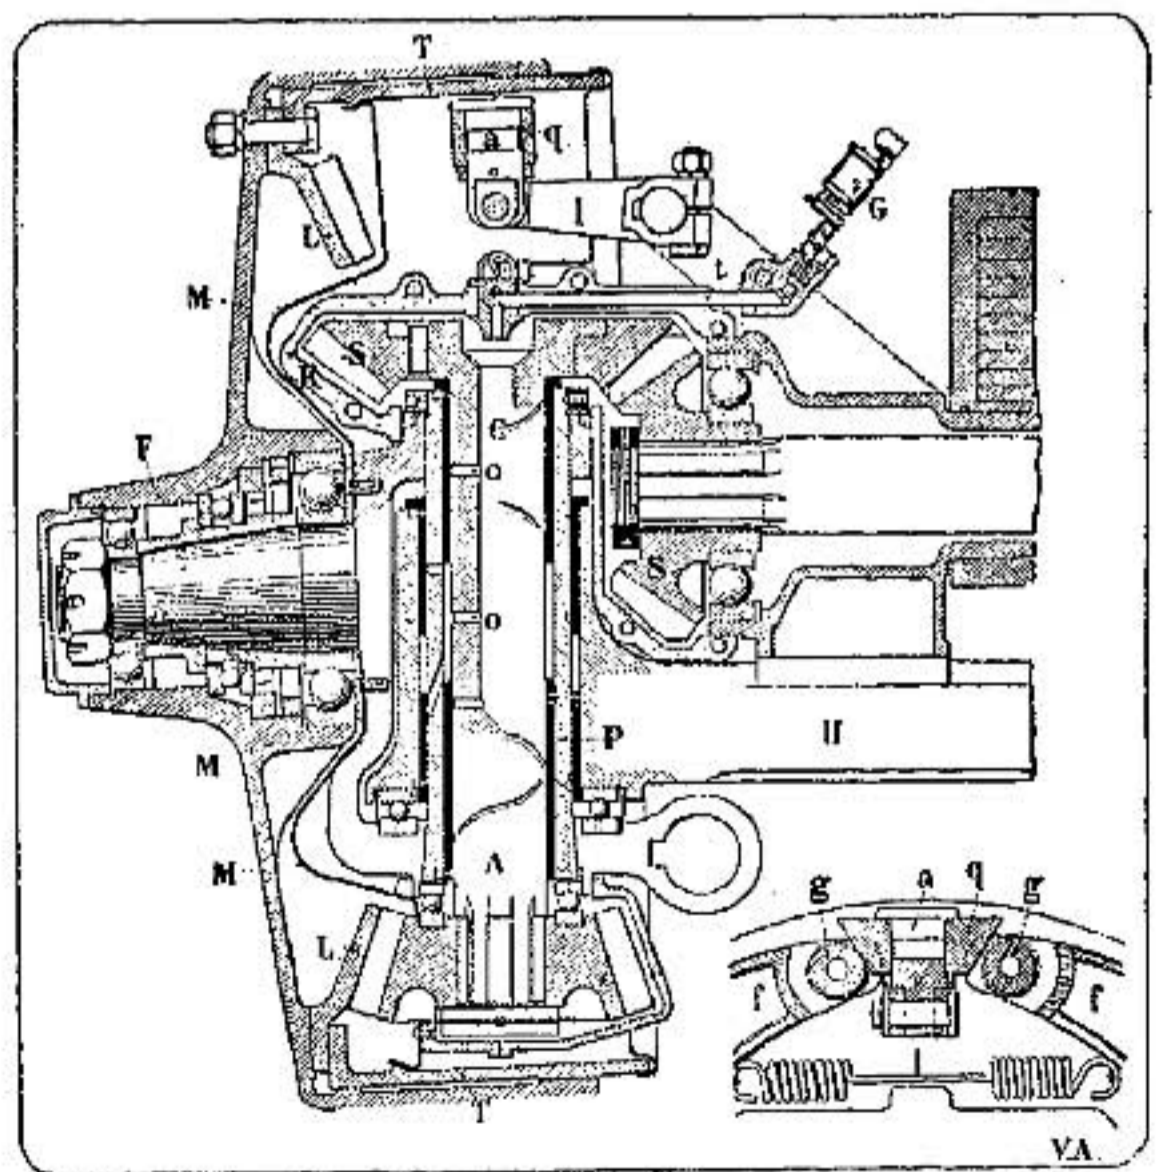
Конструкція направляющихъ и движущихъ колесъ трактора Панарь и Левассорь.
